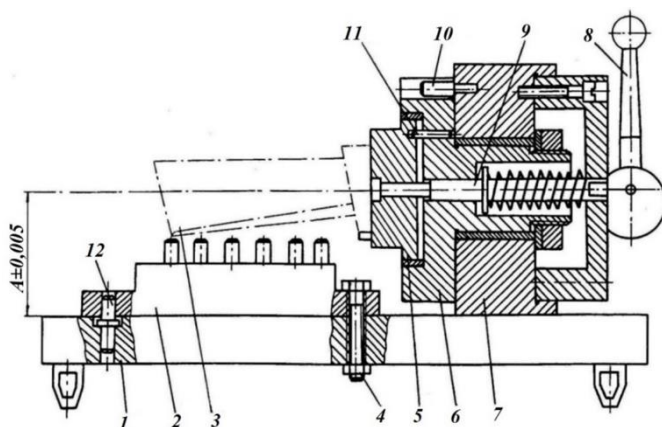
Приспособление для контроля профиля спинки и корыта рабочих лопаток компрессора
